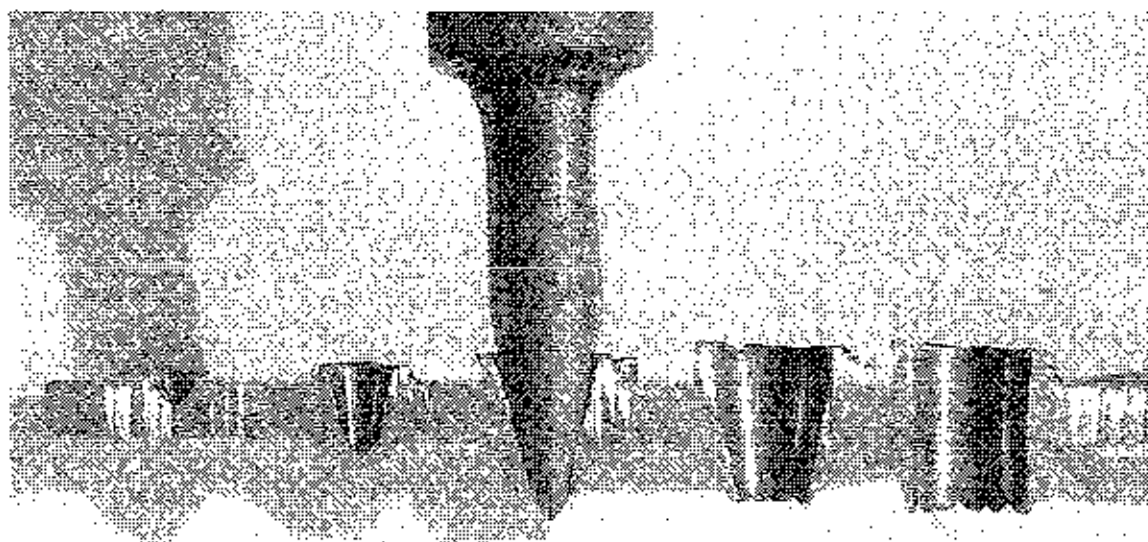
3 стадия формообразования отверстия с отбортовками
